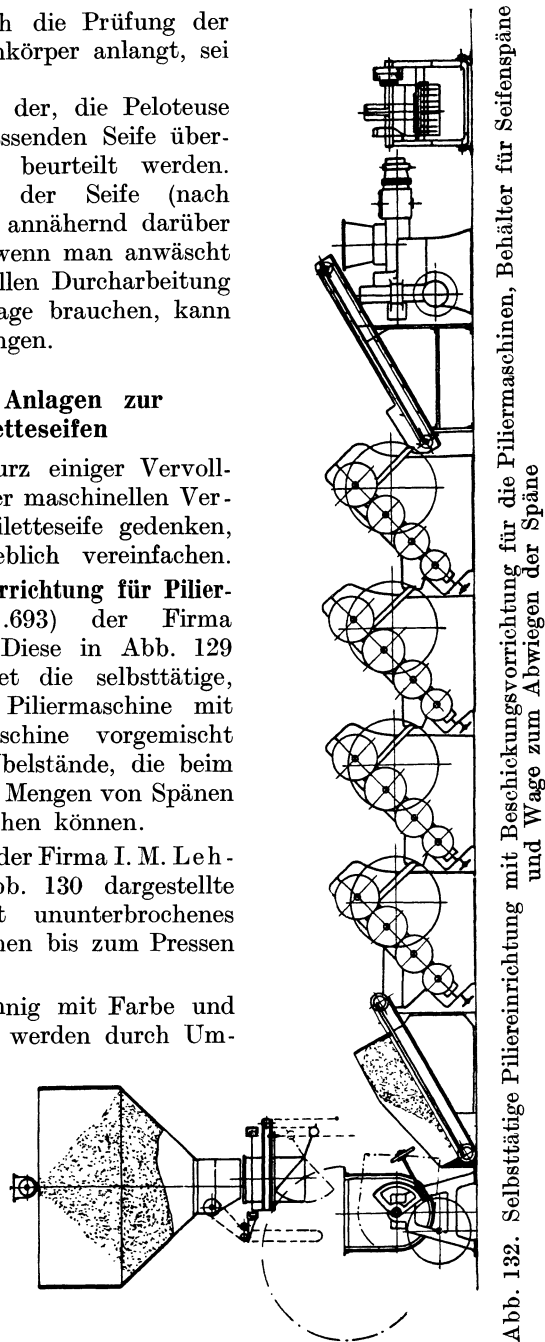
Selbsttätige Piliereinrichtung mit Beschickungsvorrichtung für die Piliemaschinen, Behälter für Seifenspäne und Wage zum Abwiegen der Späne
